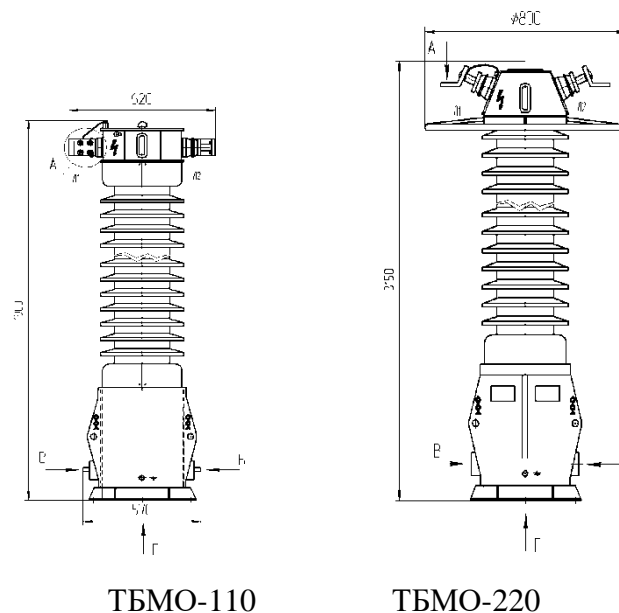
Габаритные и установочные размеры трансформаторов напряжения серии ТБМО
